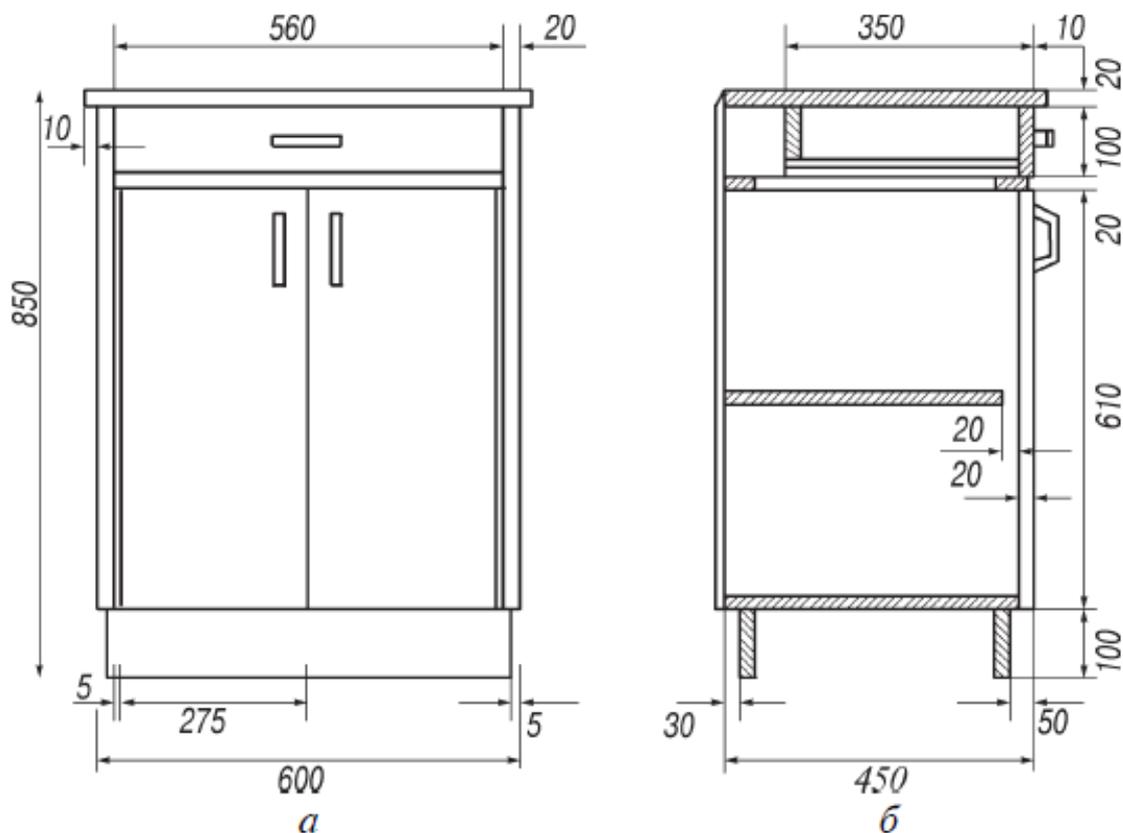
Эскиз разделочного стола-шкафа: а – вид спереди; б – поперечный разрез
